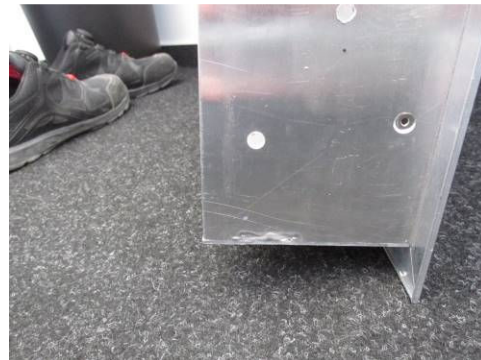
Modifiziertes Befestigungsblech angenietet, umlaufend und an den Ecken verschweißt
